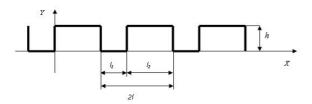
Прямоугольный профиль поверхности эталонной заготовки
